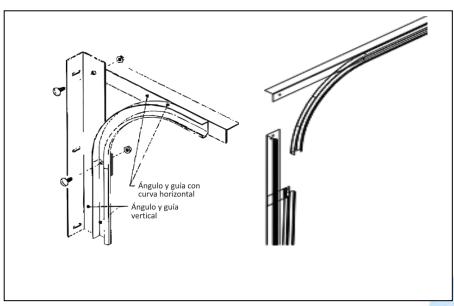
B Montaje de las guías horizontales y Platina TIPO PBI (Standard Lift)
